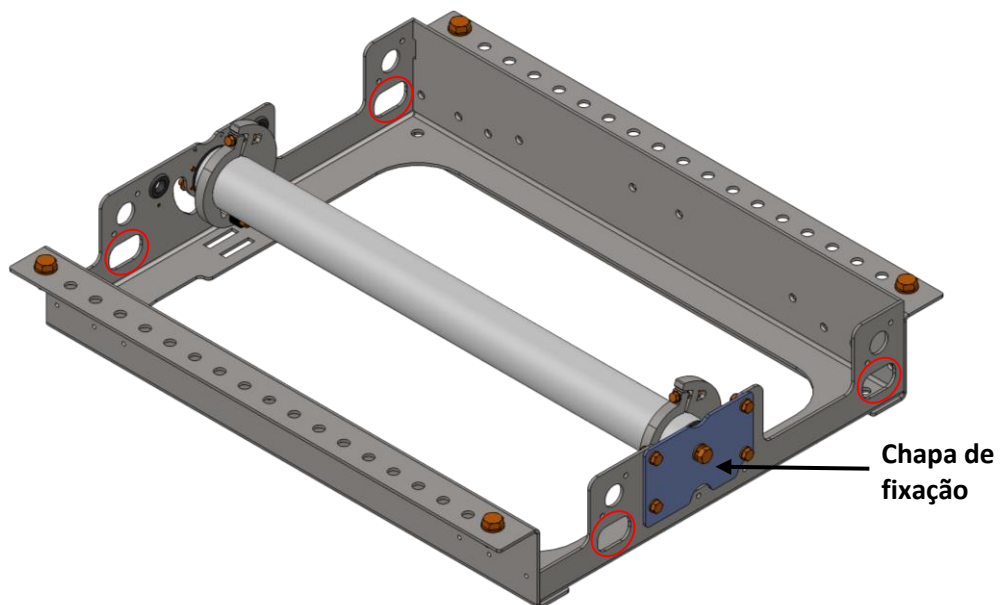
Pontos de acesso e chapa de suporte do rolo
